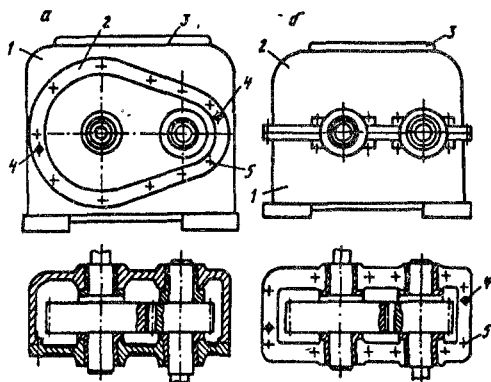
Конструкции редукторов, позволяющих осуществлять осевую (а) и поперечную (б) системы сборки
